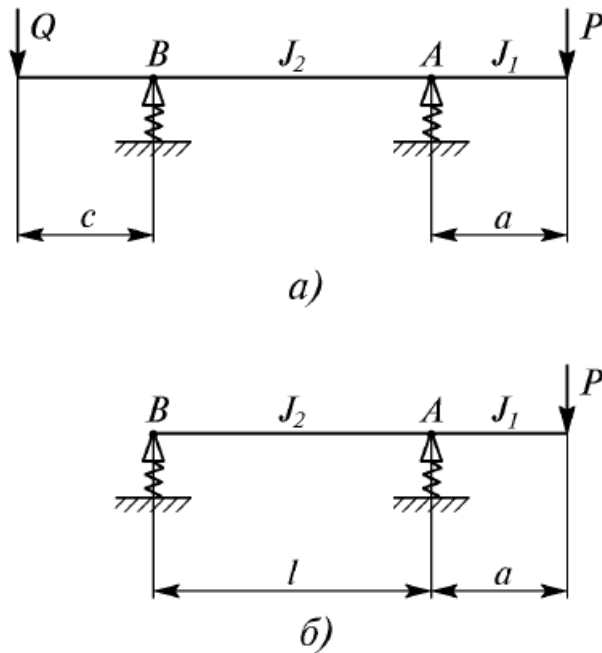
Схеми к розрахунку шпиндельного вузла на жорсткість
